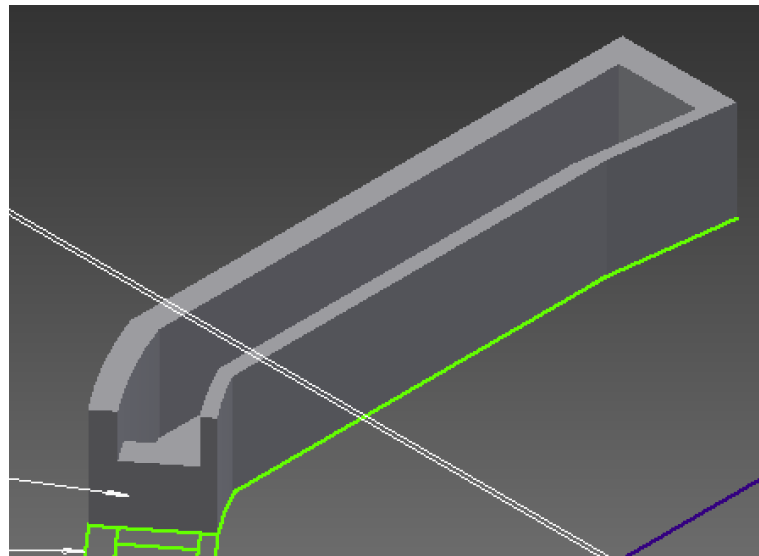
Vista frontal lateral izquierda desde arriba de pieza del lado izquierdo.
